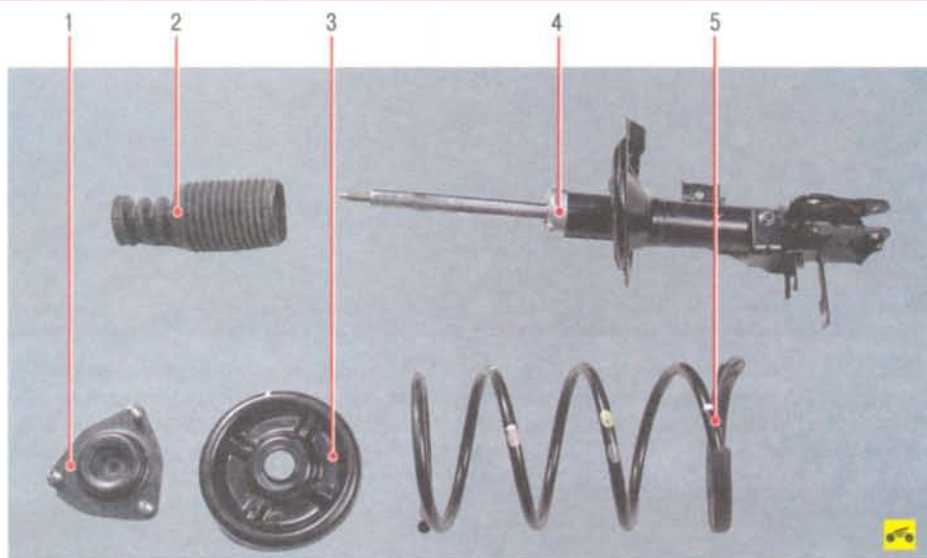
Детали передней амортизаторной стойки: 1 – верхняя опора стойки; 2 – защитный чехол; 3 – верхняя опорная чашка пружины; 4 – амортизатор; 5 – пружина
